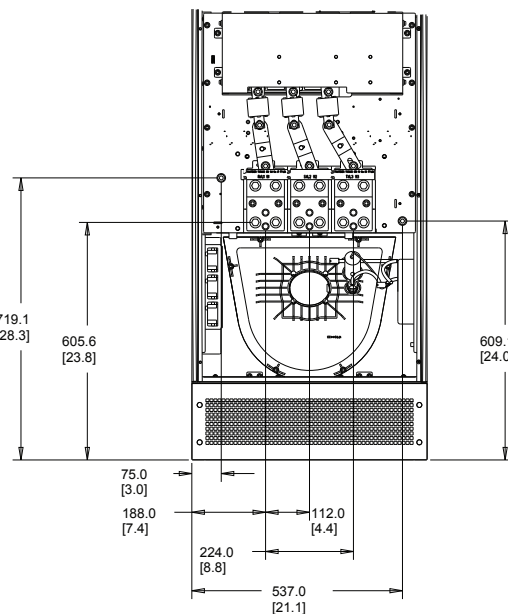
Расположение клемм в корпусе E1 без разъемника
